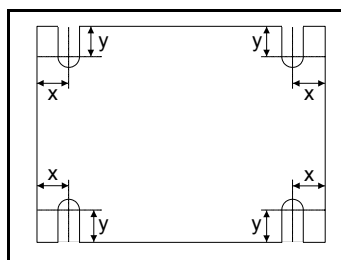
Габаритные размеры индуктора фильтра частоты ШИМ типа 1
